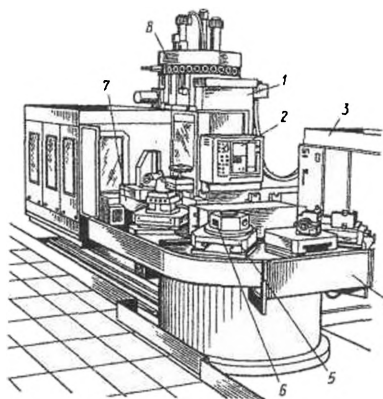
Гнучкий виробничий модуль для виготовлення корпусних деталей
